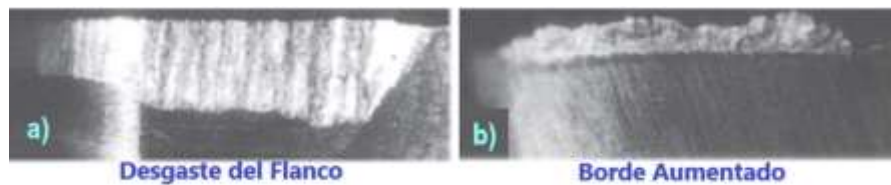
Tipos de desgaste en herramientas de corte: a) Desgaste en el flanco de un inserto herramienta de corte y b) borde aumentado por material de trabajo mecanizado. [55]
